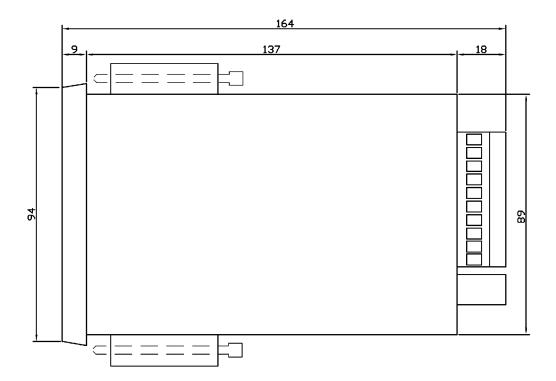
Габаритные размеры щитового варианта указателя положения РПН ${\rm У}\Pi 23 \ ({\rm типоразмер}\ \Gamma)$
